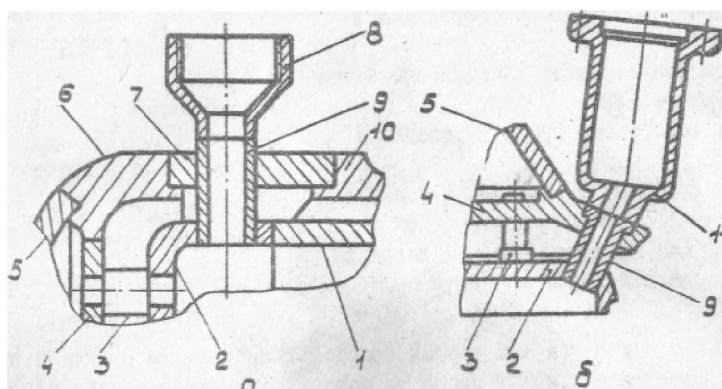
Схемы установки воспламенителя: а – на кольце, соединяющем смесительную головку с корпусом; б – на корпусе смесительной головки; 1 – стенка корпуса камеры, 2 – внутреннее днище, 3 – форсунка, 4 – среднее днище, 5 – наружное днище, 6 – корпус головки, 7 – соединительное кольцо, 8 – штуцер для установки пиросвечи, 9 – переходная втулка, 10 – корпус камеры, 11 – корпус пиросвечи
